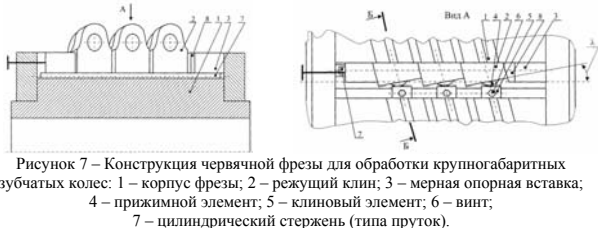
Конструкция червячной фрезы для обработки крупногабаритных зубчатых колес: 1 – корпус фрезы; 2 – режущий клин; 3 – мерная опорная вставка; 4 – прижимной элемент; 5 – клиновидный элемент; 6 – винт; 7 – цилиндрический стержень (типа прутков).
